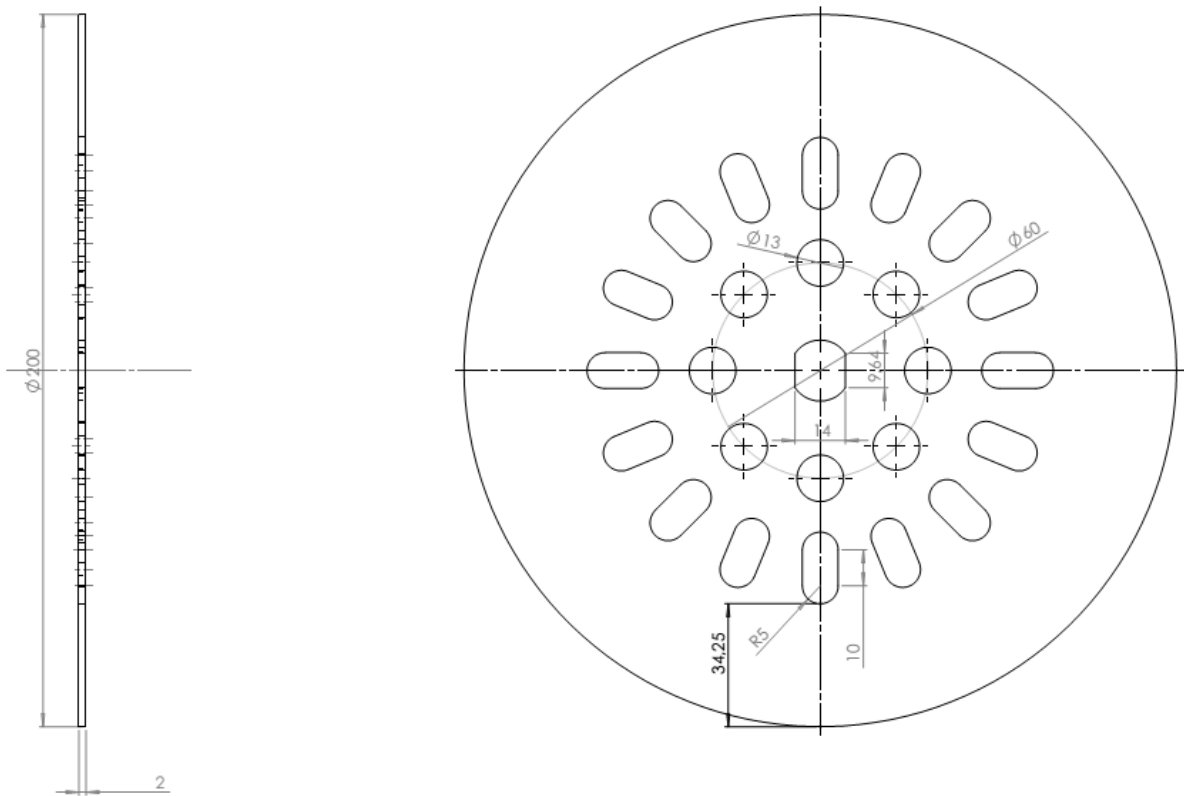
Dimensões (em milímetros) dos discos do rotor tipo F.
